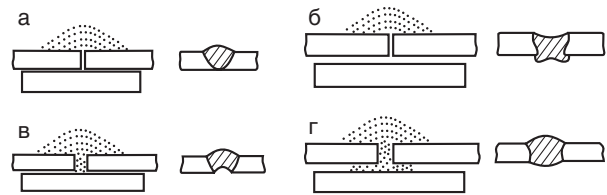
Схема односторонней автоматической сварки стыковых соединений на медной подкладке
